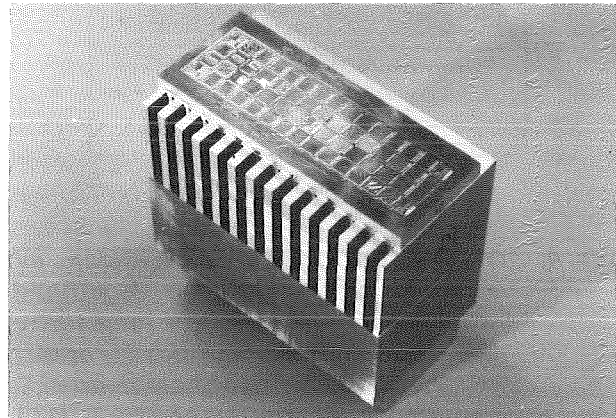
LIGA-Abformwerkzeug, dessen Formabweichungen der Werkzeugstirnfläche mit Hilfe einer Spannvorrichtung auf weniger als $\pm 5 \mu\text{m}$ Durchbiegung reduziert wurde [5].
